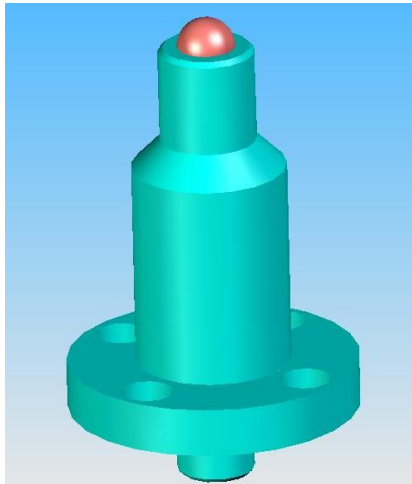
Apoio para a ligação ao "Ball-Joint"
